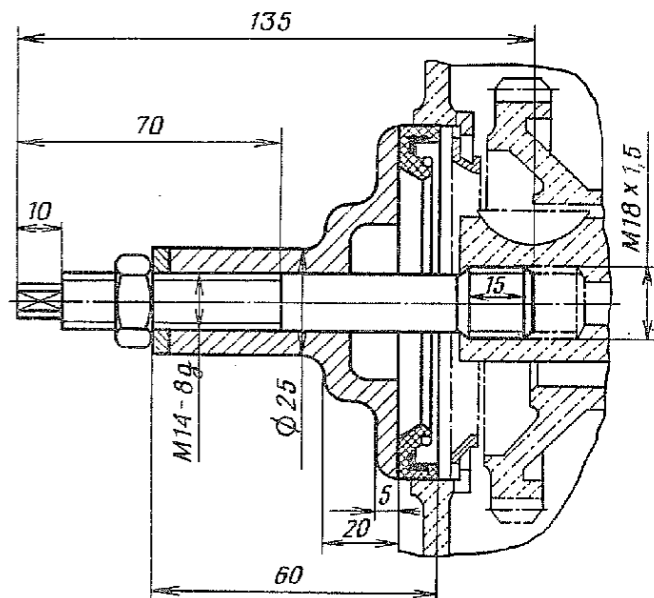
Оправка для запрессовки сальника коленчатого вала со стороны центробежного маслоочистителя
